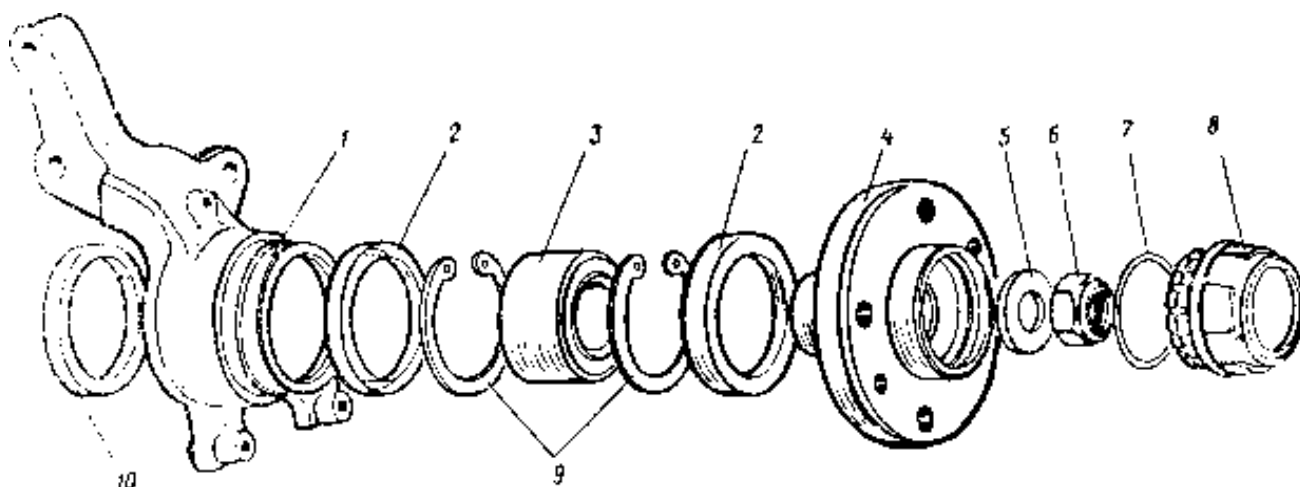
Поворотна цапфа і деталі маточини переднього колеса
